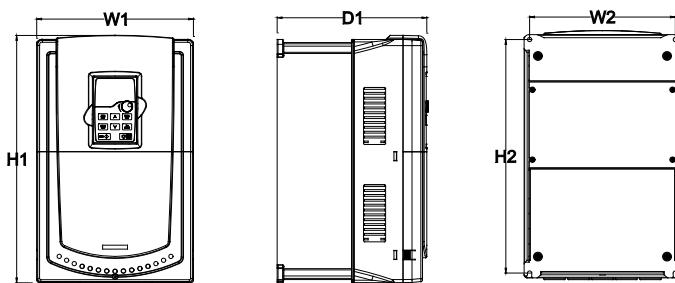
Настенный монтаж 1.5 – 30 кВт
